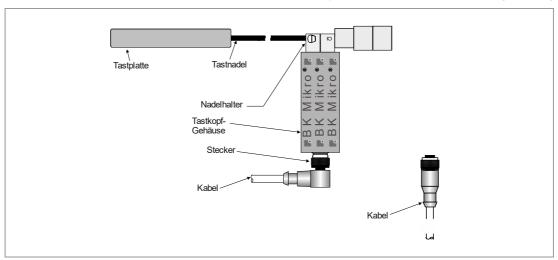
Tastkopf mit Tastnadel für axiale Werkzeugabtastung
